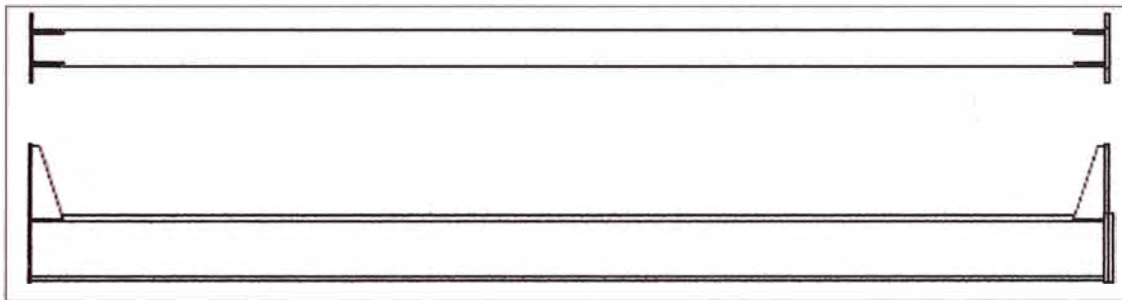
Planta y Elevación del Carril Simple L=6.79m.
